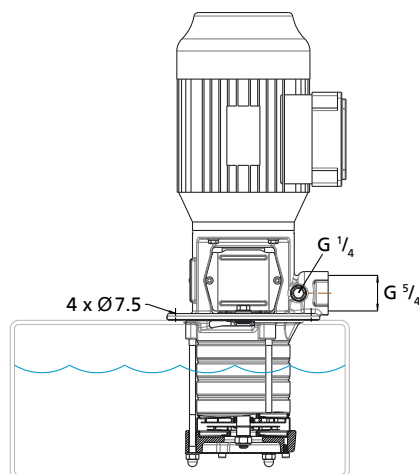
[TPG-20130303-A]: Pumpenaggregat ausbauen
